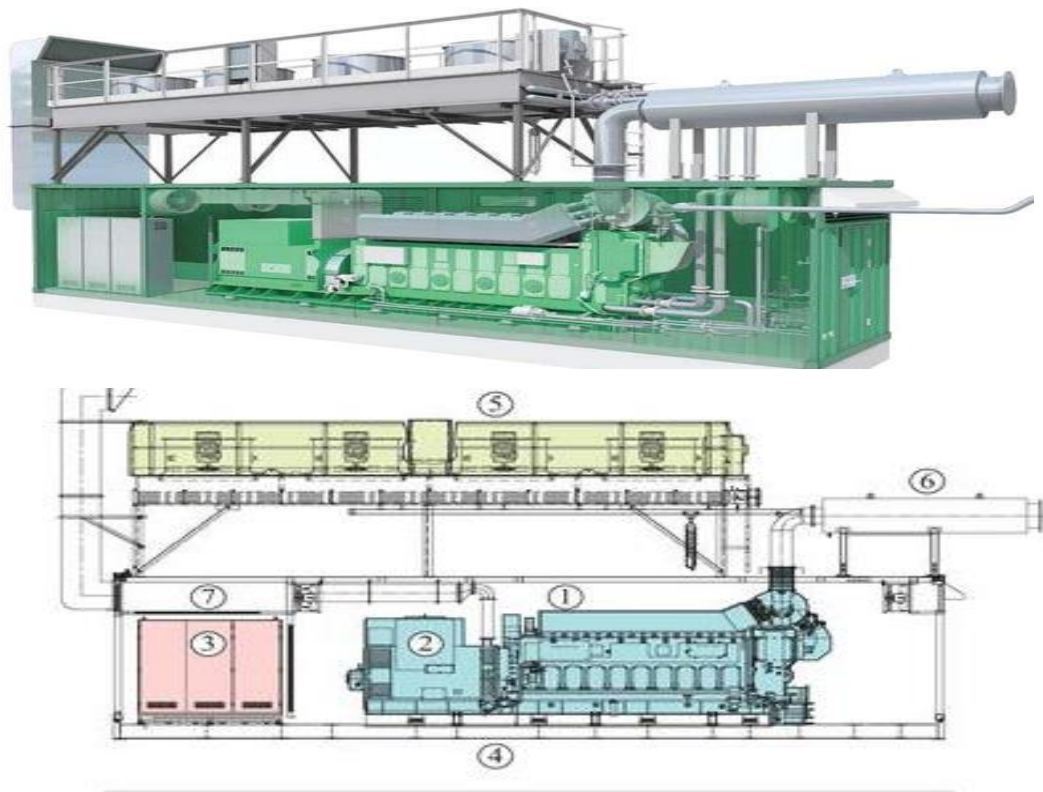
Vue d'ensemble d'une centrale thermique diesel (sans salle des machines) [22]
